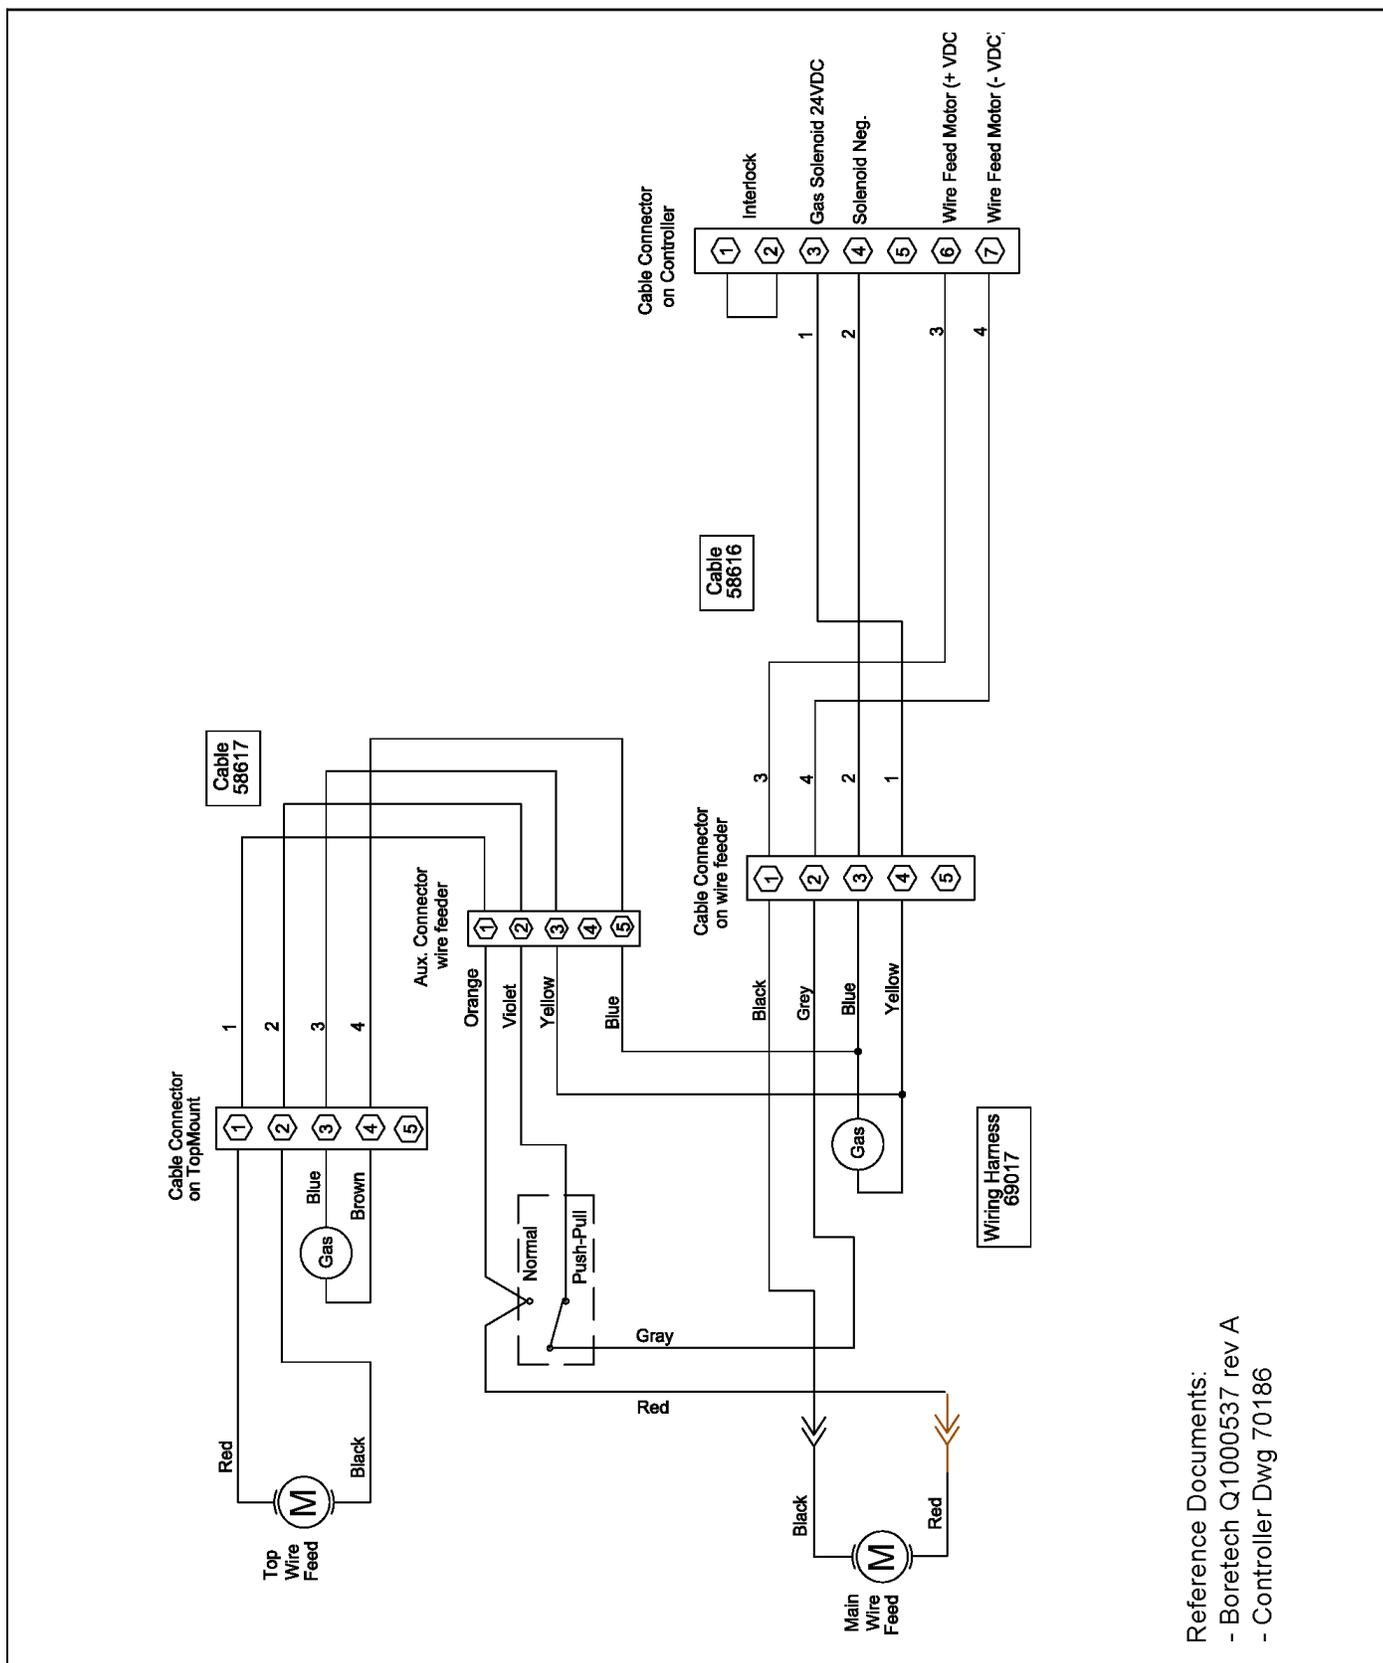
СХЕМА Станка с МЕТАЛЛИЧЕСКИМИ и ПЛАСТИКОВЫМИ РАЗЪЕМАМИ (КАТ. № 87413)
